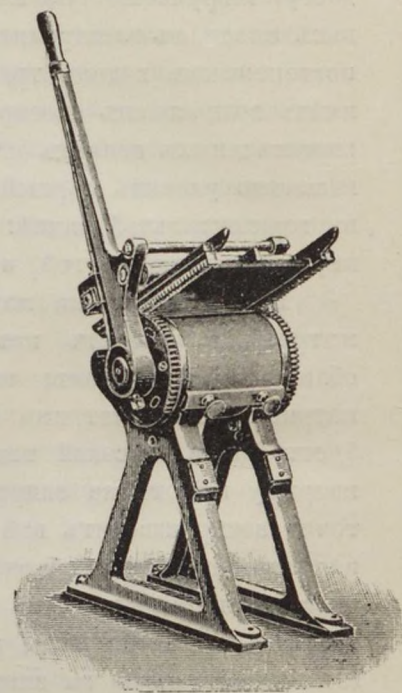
Приспособленіе для выгибанія гальвано согласно кривизнѣ цилиндровъ ротативныхъ машинъ.
